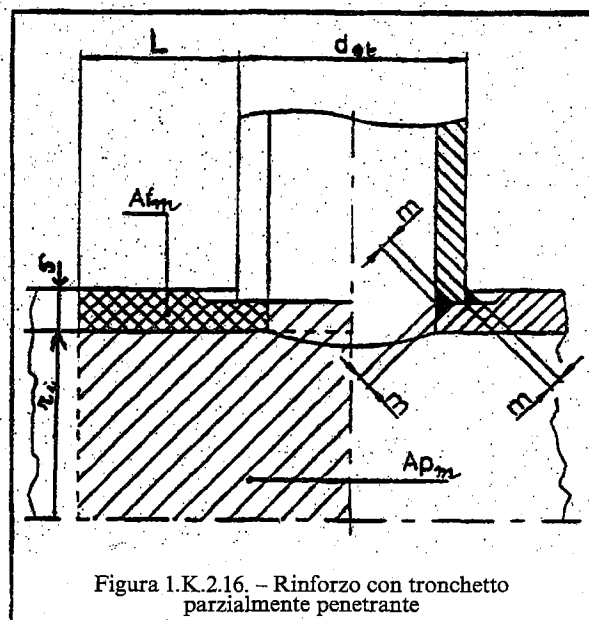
K.2.16. – Rinforzo con troncetto parzialmente penetrante
